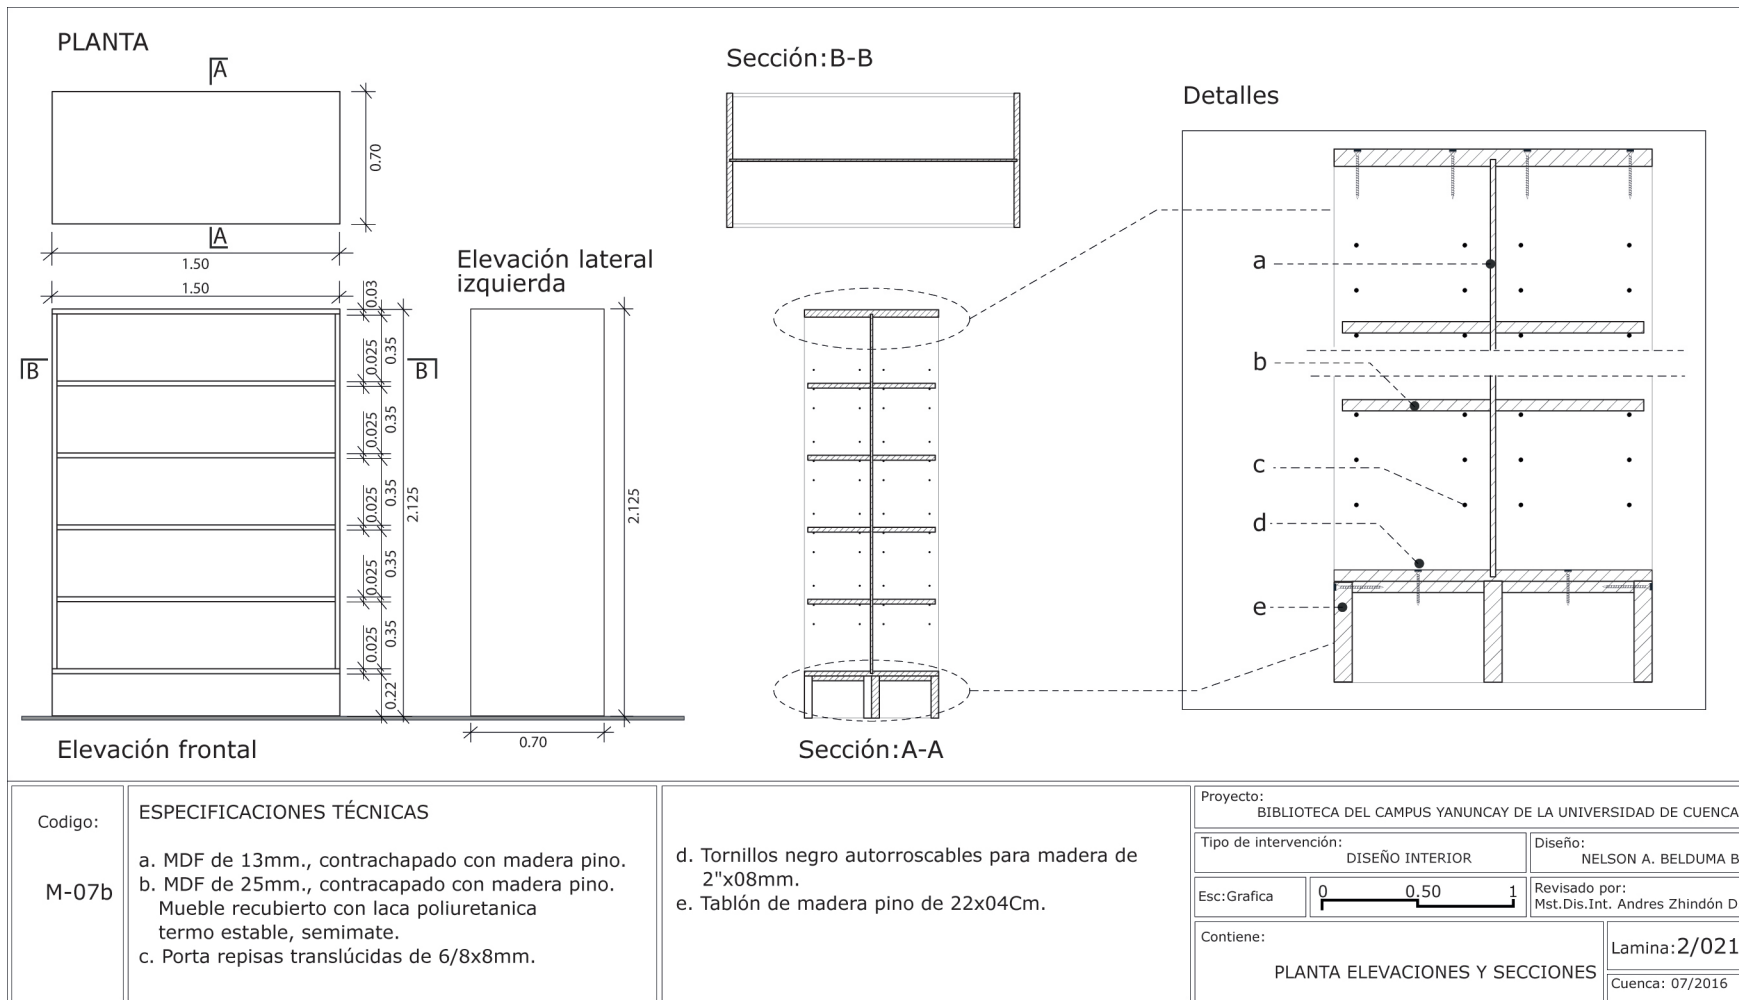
Planta, elevaciones y secciones. Estanterías. M-07b.
